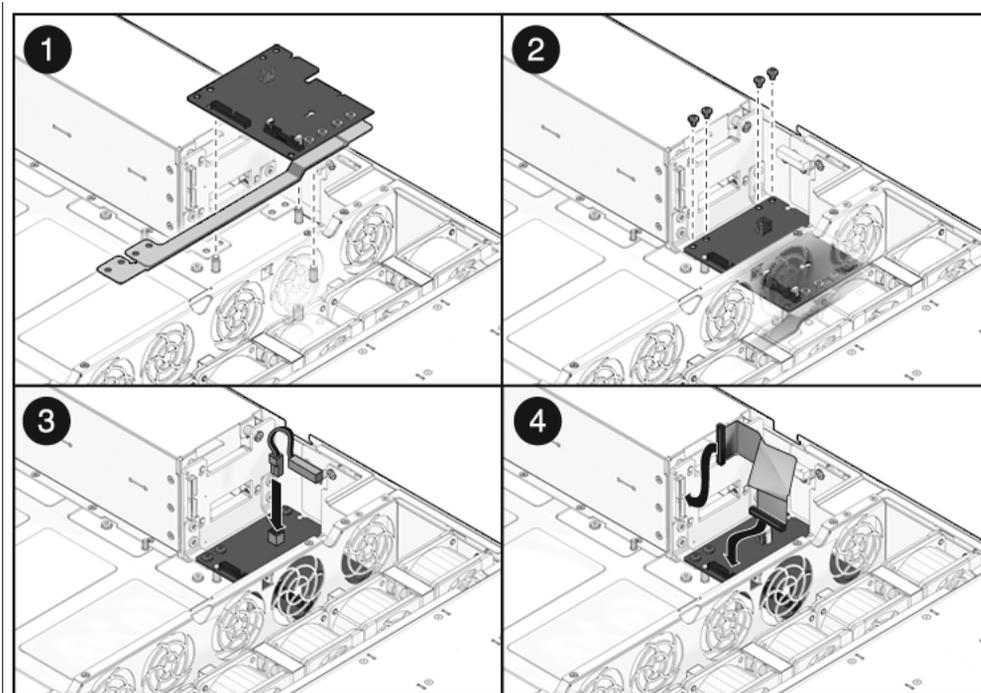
Installazione della scheda di distribuzione dell'alimentazione (server Sun SPARC Enterprise T5140)
